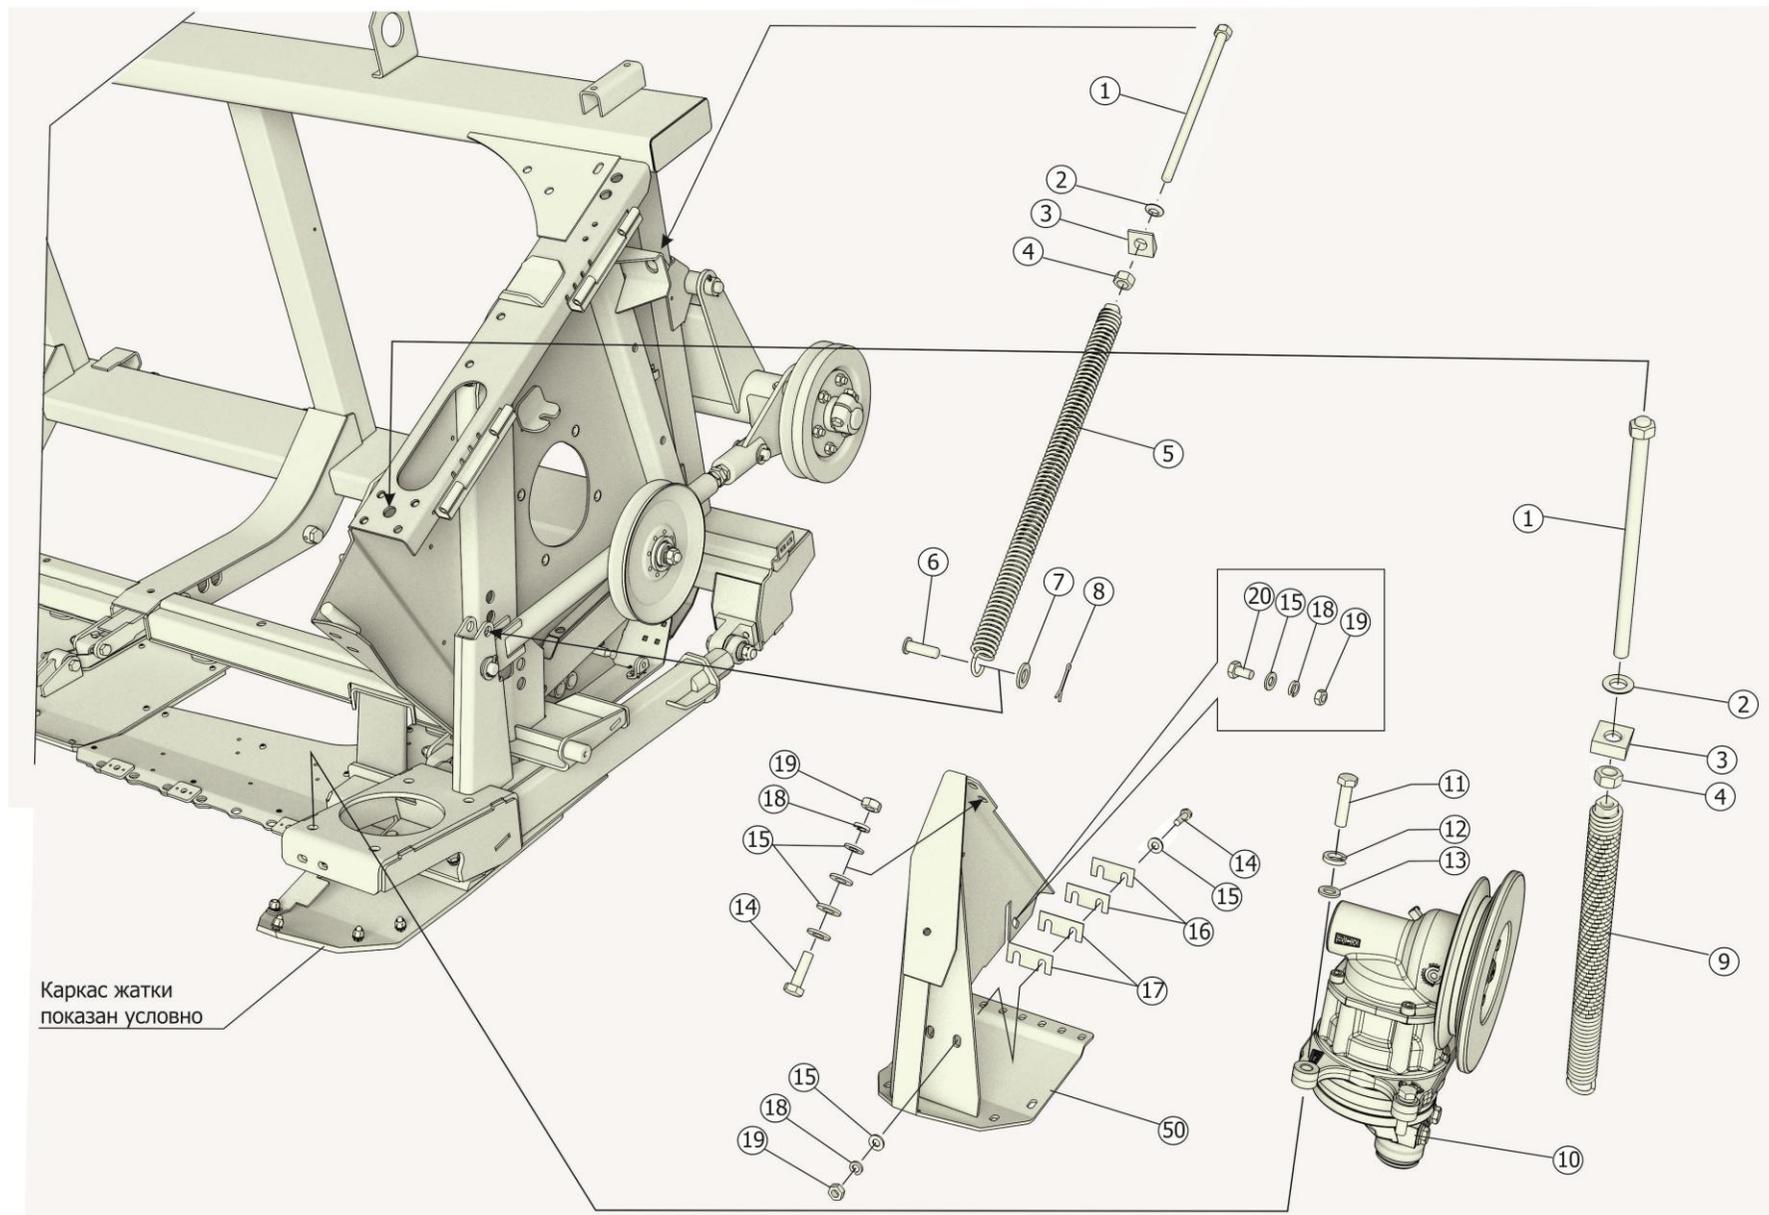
Привод режущего аппарата ЖСУ-703.01.03.500Б
